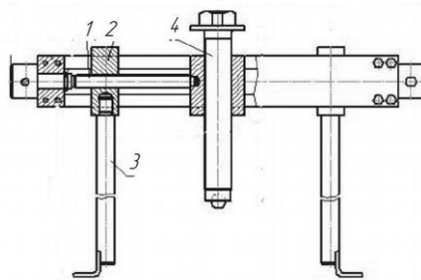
Знімач універсальний для випресовування підшипників із гнізд корпусів мод. Kraftool 1-43310-130: 1 – маточина-гайка; 2 – регульовальний гвинт; 3 – захват; 4 – віджимний болт
